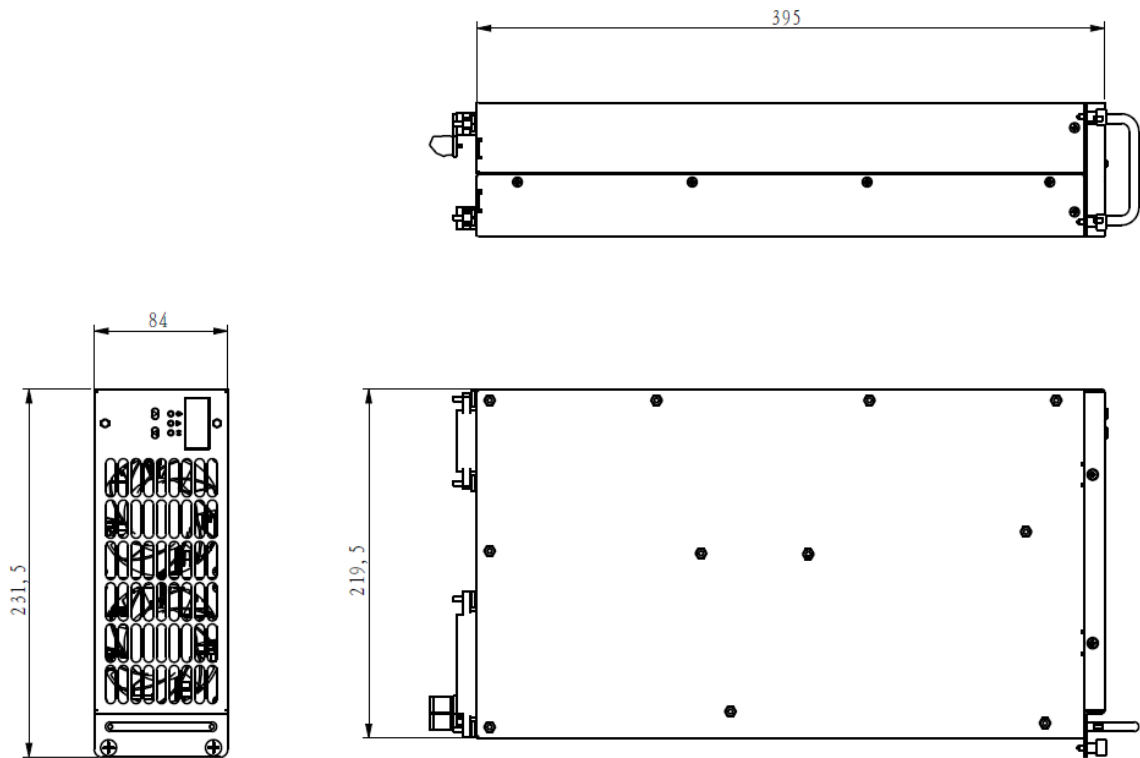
모듈 가로 배치 사이즈 (단위 : mm)
